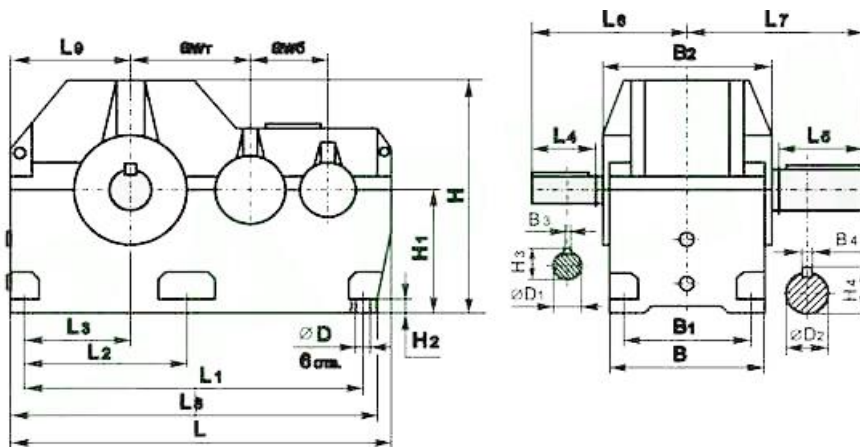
Габаритні та з'єднувальні розміри редуктора
